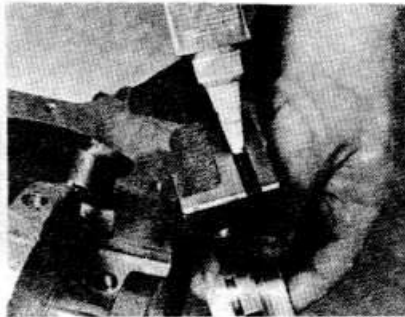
Заполните боковые пазы крышки заднего коренного подшипника пастой для уплотнения стыков...
